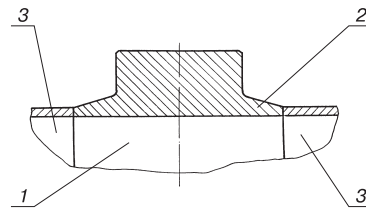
Бандаж сварной: 1 – бандаж; 2 – закрывки банджа; 3 – обечайки корпуса
